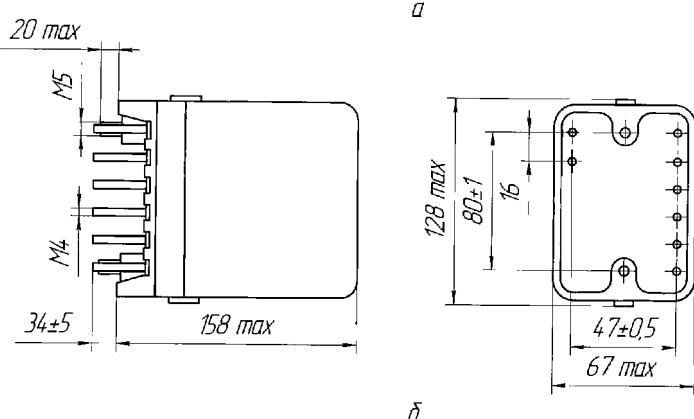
Габаритные, установочные и присоединительные размеры реле типа PCB-01-5.
